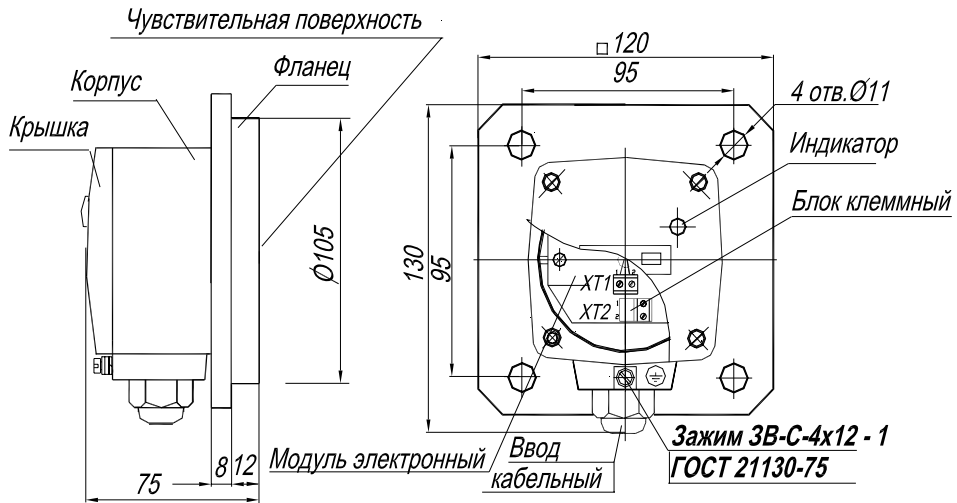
Внешний вид и габаритные размеры датчика
